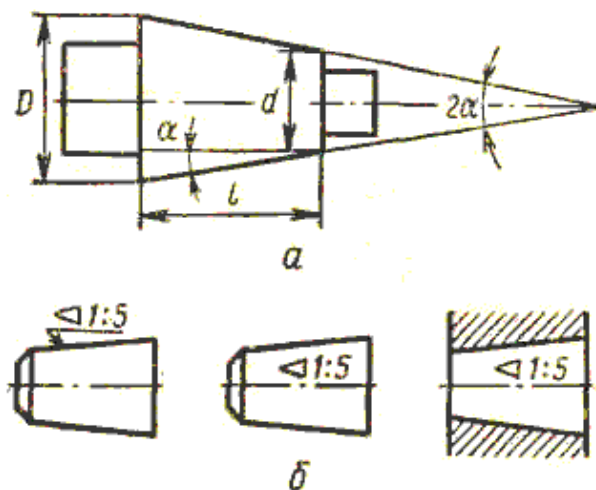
Элементы конической поверхности (а), условные обозначения конусности на чертежах (б)
